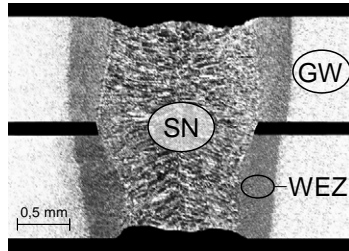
Gefügeausbildung beim Laserstrahlschweißen; Werkstoff H320LA, Blechdickenkombination 1,0/1,0 mm, $P_L = 3,5$ kW, $d_f = 0,68$ mm, $v_s = 3,8$ m/min.
